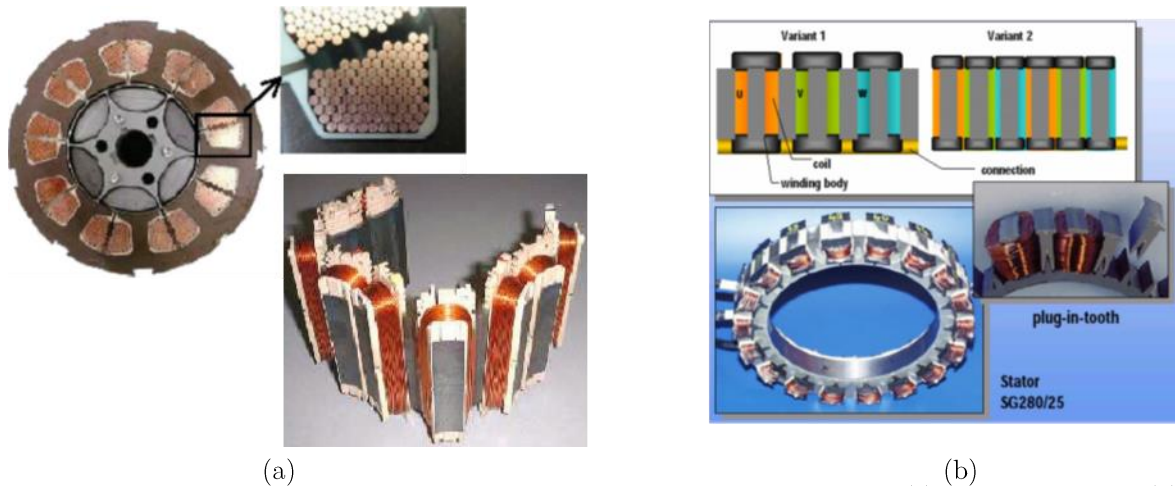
Techniques d'assemblage d'un stator dans le cas d'un bobinage dentaire, (a) joint-lapped stator, (b) plug-in-tooth [7]
